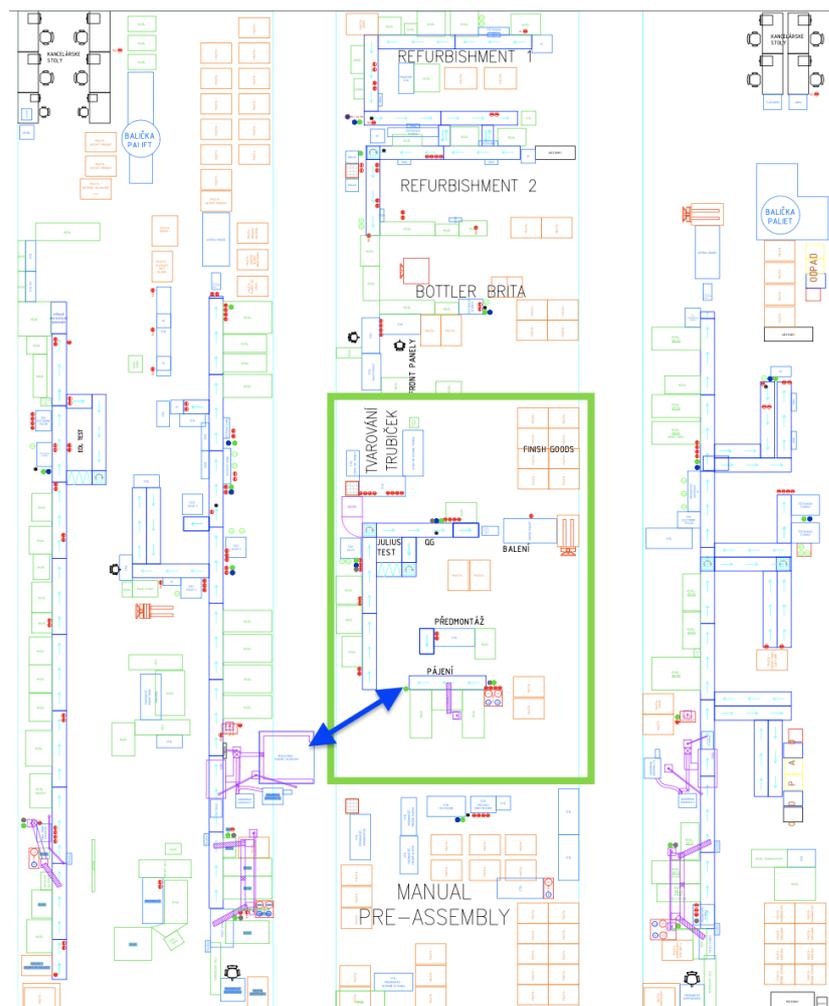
Varianta layoutu C (vlastné spracovanie)
